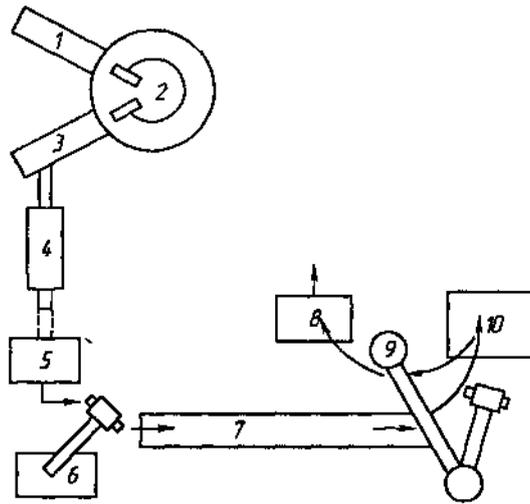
Схема поточной линии штамповки коленчатых валов с использованием роботов: 1 – автоматический загрузчик; 2 – круговая печь с поворотным подом; 3 – разгрузочный механизм; 4 – автоматический подаватель; 5 – заготовительный молот; 6, 9 – роботы; 7 – пластинчатый конвейер; 8 – обрезной пресс; 10 – штамповочный молот
